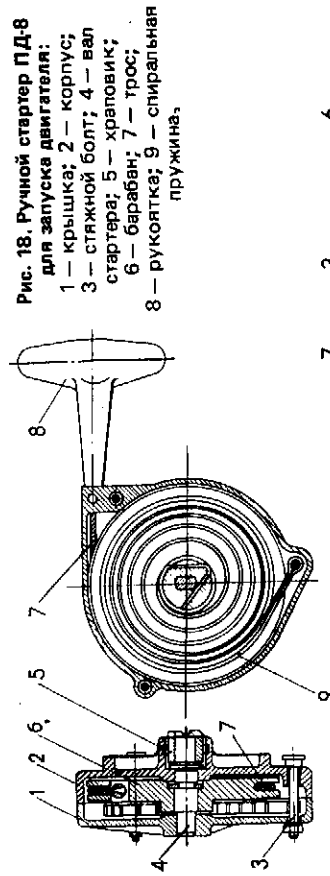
Ручной стартер ПД-8 для запуска двигателя:
